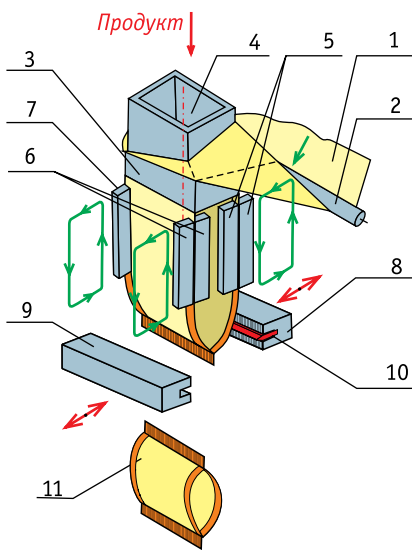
Технологічна схема упаковочної машини періодичного дійства з воротниковим рукавообразувателем і тянущими губками продольного сваривання
